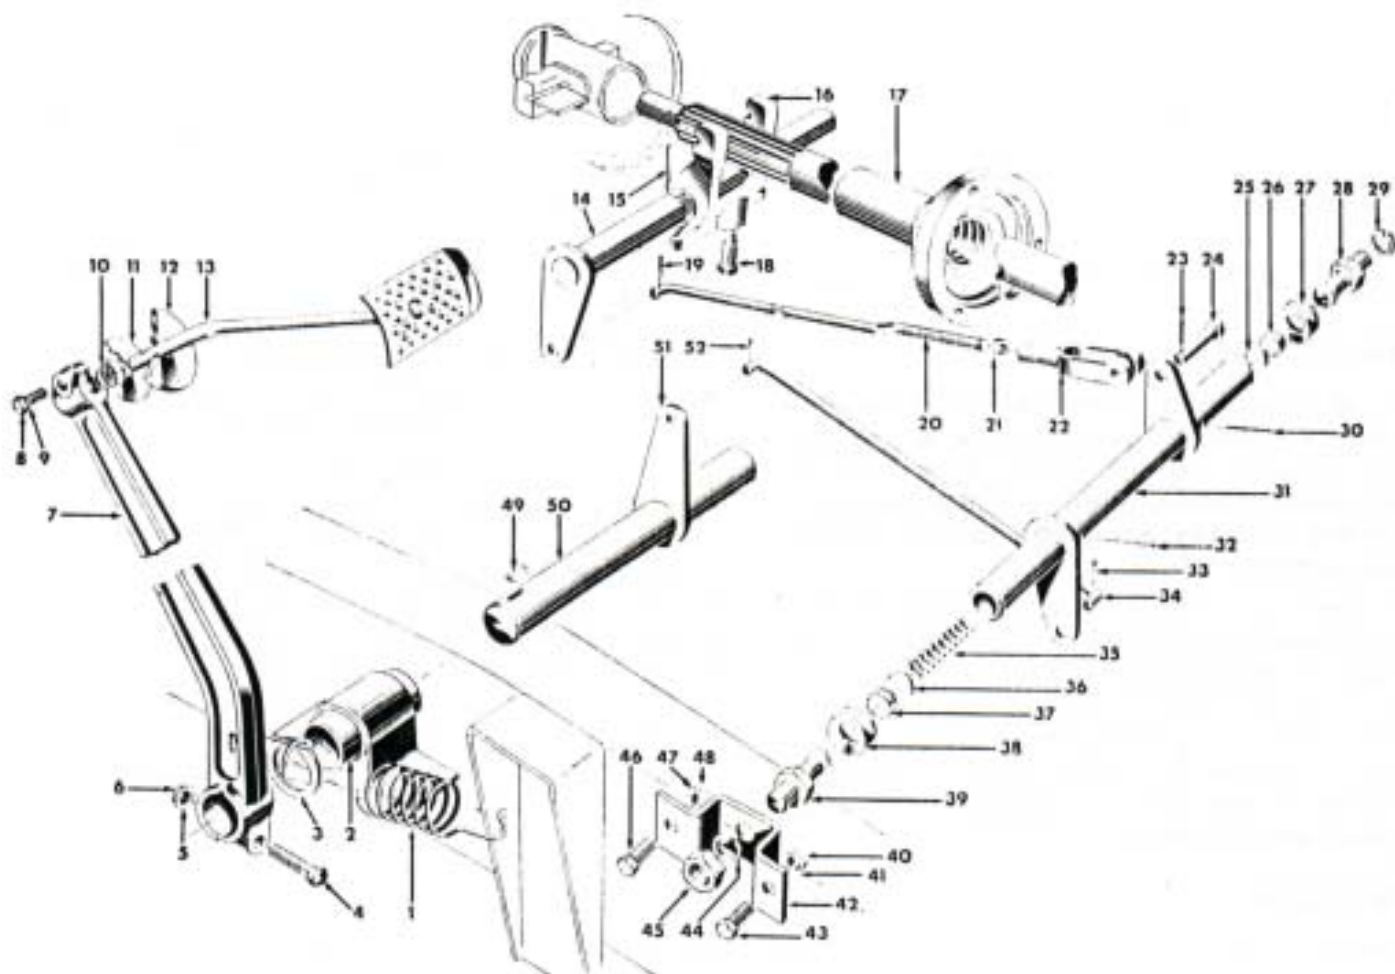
Despiece del mecanismo de mando del embrague (Jeep).
